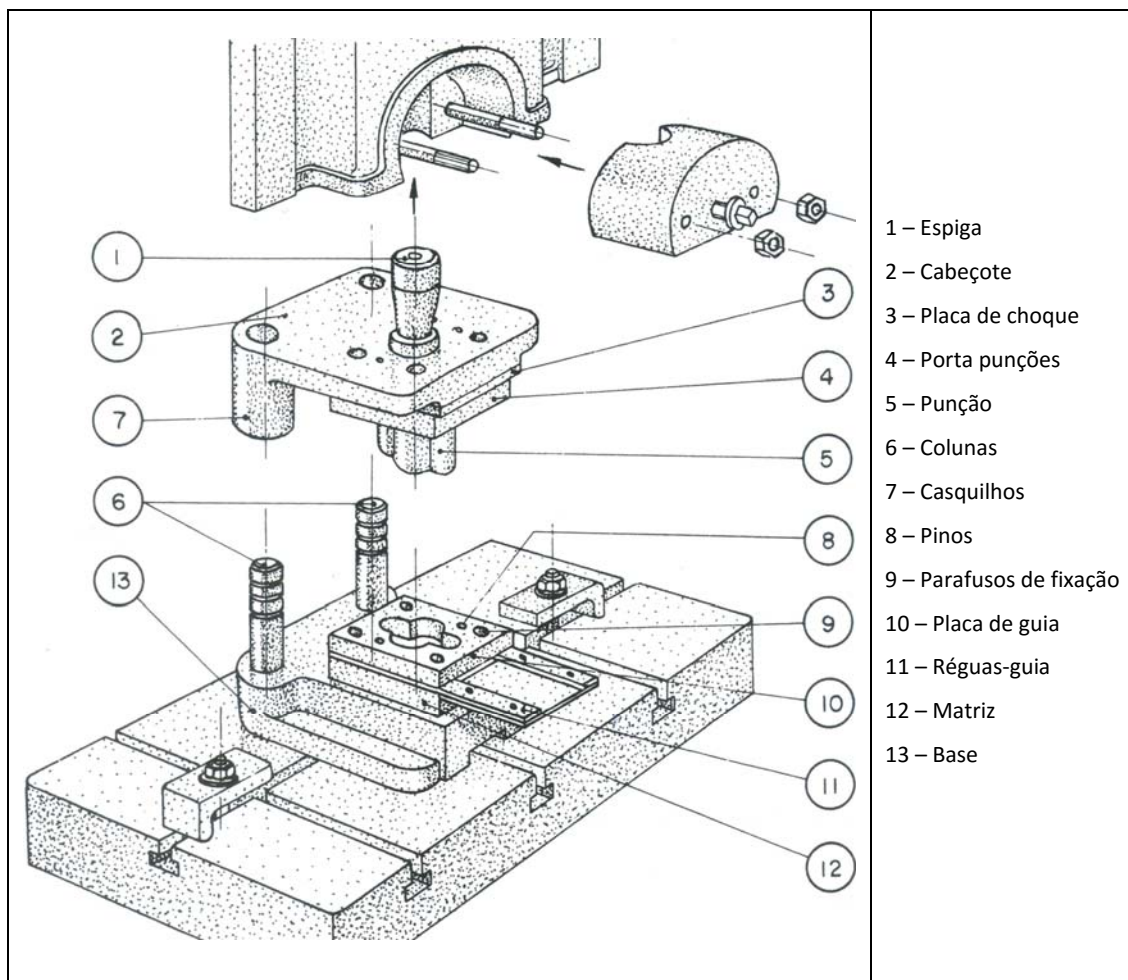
Elementos de um ferramenta de estampagem/corte ³⁰
